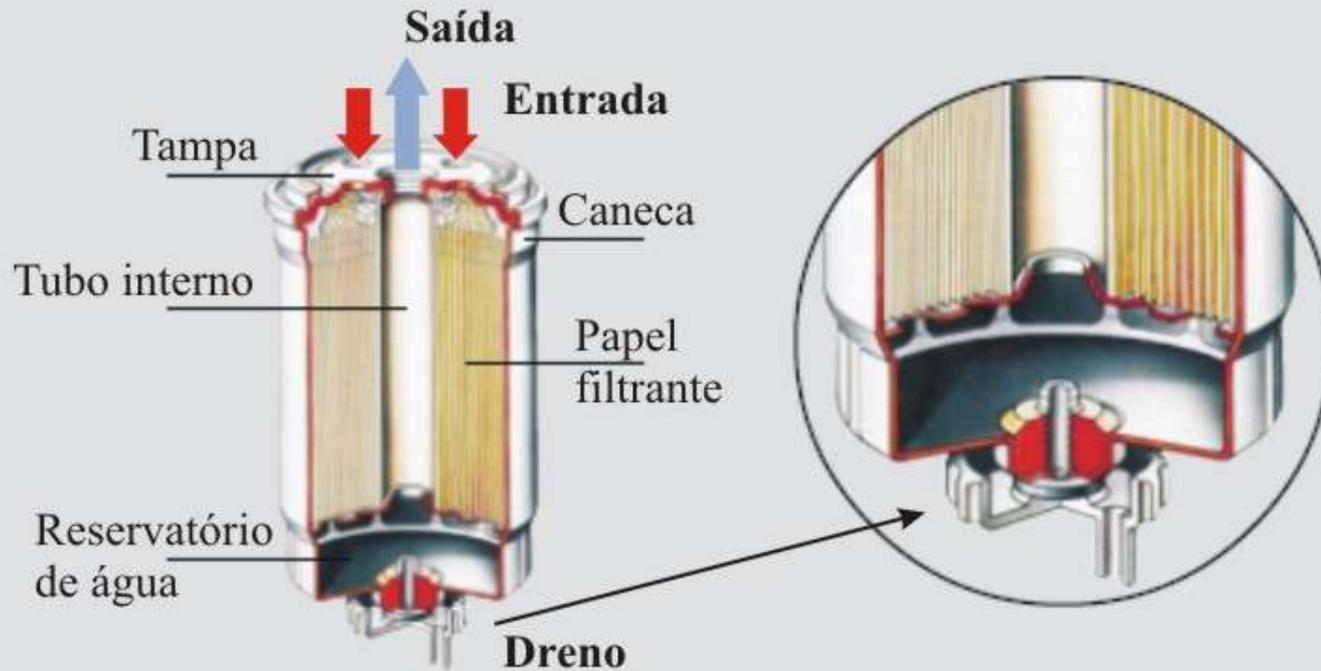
Filtro de combustível para motores diesel e seus componentes.
